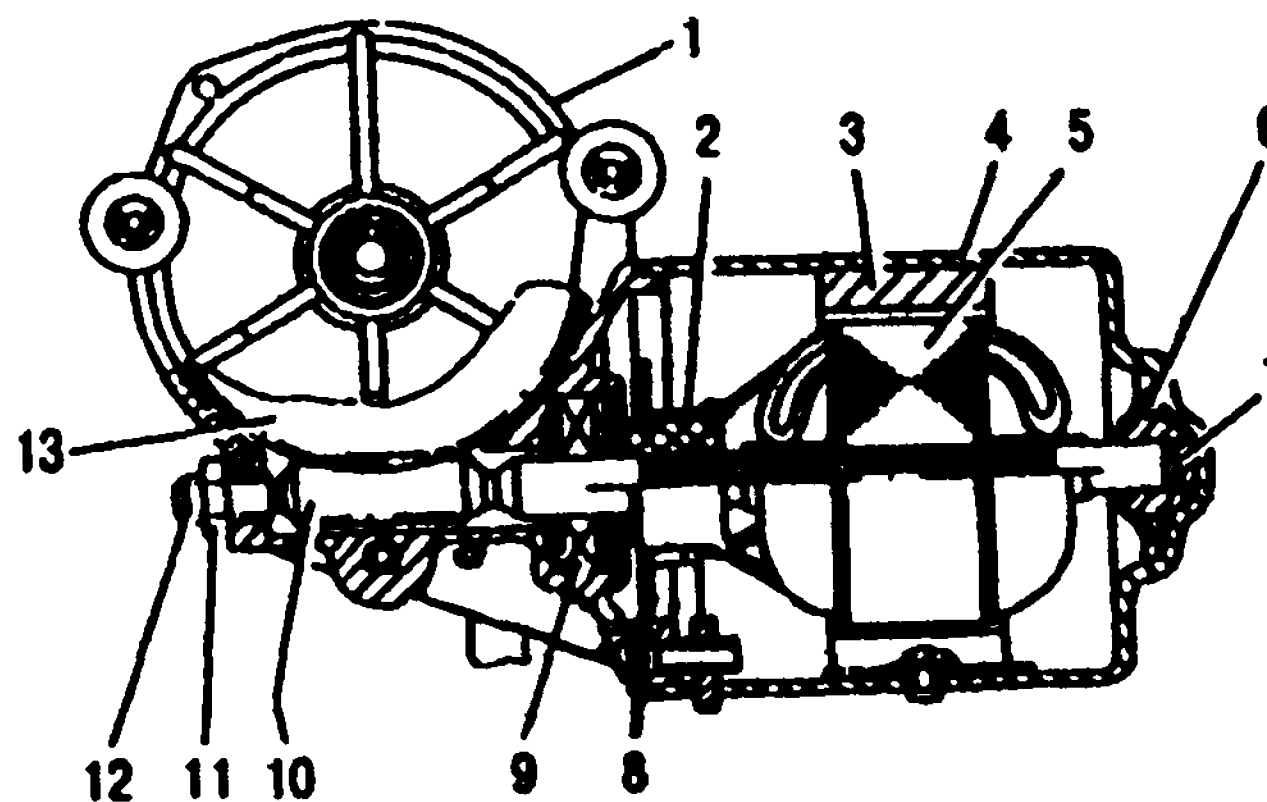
Моторредуктор стеклоочистителя: 1 - корпус редуктора, 2 - коллектор, 3 - постоянный магнит, 4 - корпус электродвигателя, 5 - якорь, 6 - подшипник, 7 - шарик упорный, 8 - панель щеткодержателей, 9 - подшипник шариковый, 10 - червяк, 11 - гайка стопорная, 12 - винт упорный, 13 - шестерня
